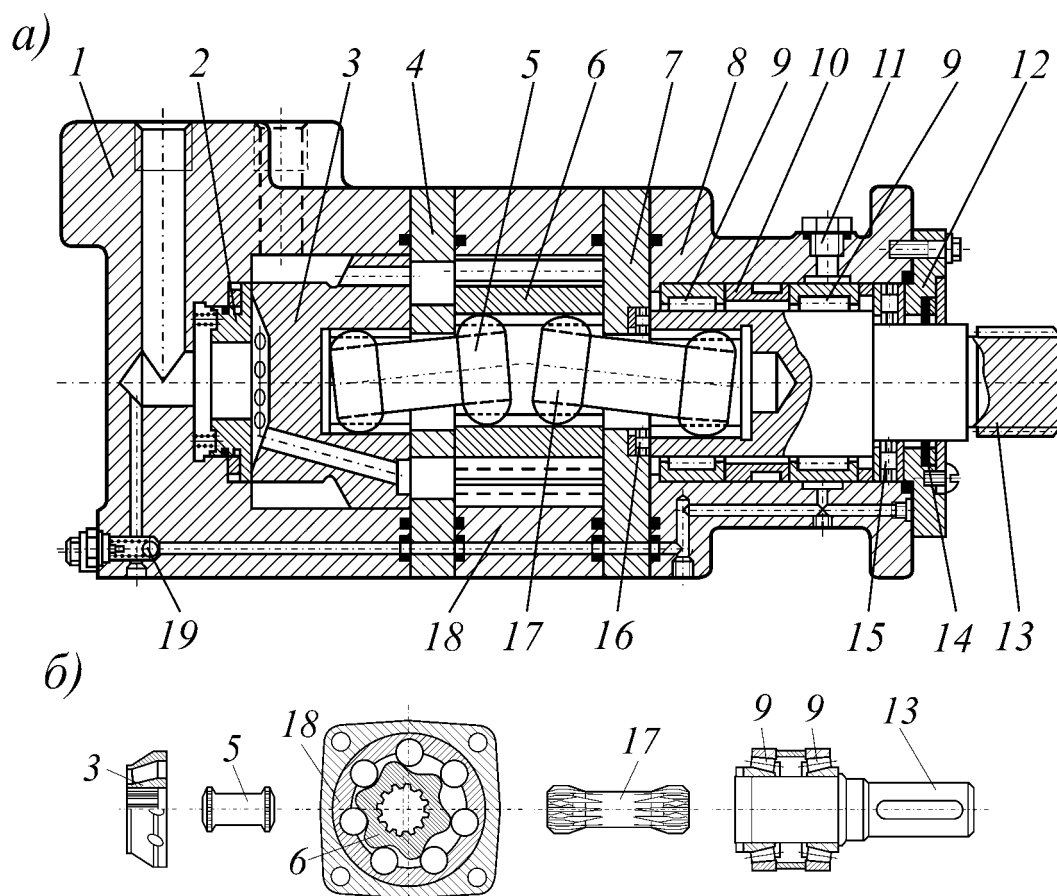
Героторный гидромотор: а) устройство гидромотора: 1 – корпус; 2, 10 – втулки; 3 – распределительный диск; 4 – разделительный диск; 5, 17 – промежуточные зубчатые валы; 6 – ротор; 7 – диск; 8 – корпус подшипникового узла; 9, 15, 16 – подшипники качения; 11 – дренажный штуцер; 12 – крышка; 13 – вал; 14 – уплотнительное кольцо; 18 – статор; 19 – обратные клапаны дренажной системы; б) основные элементы движущей системы мотора
